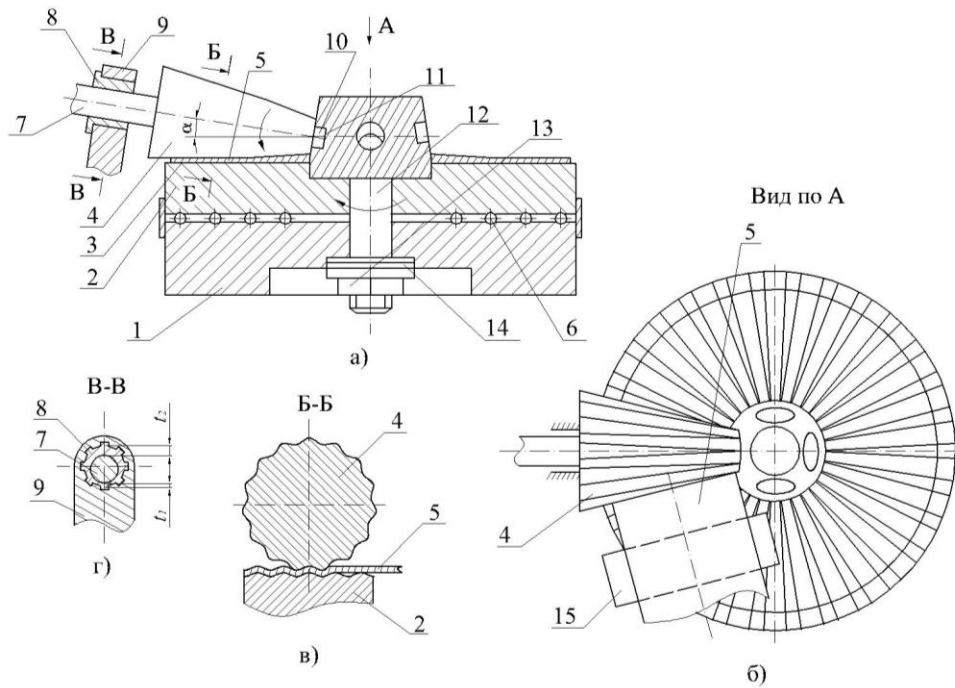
Пристрій для виготовлення гофрованих гвинтових заготовок кінцевими формуючими елементами:
